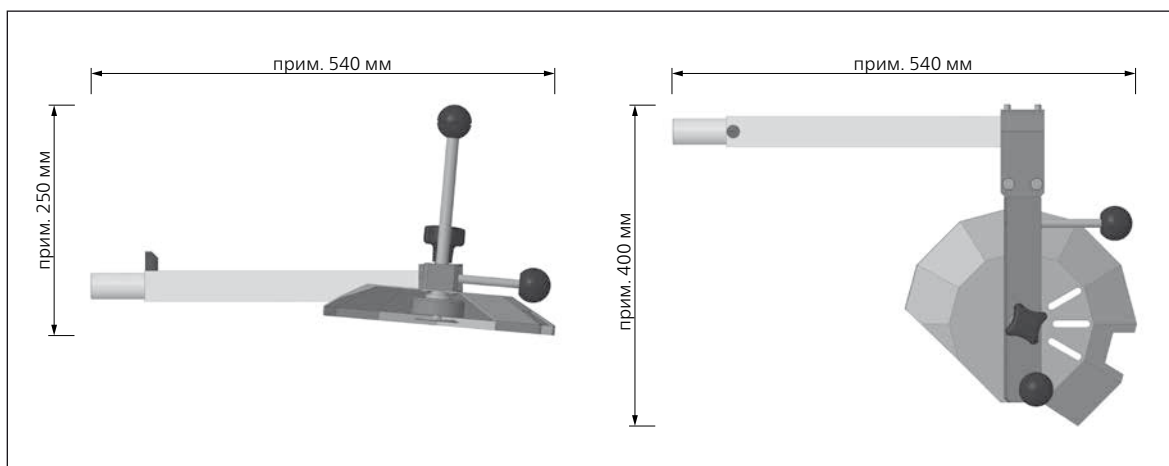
Размеры в мм (HV 205-1, вид спереди/вид сверху)
